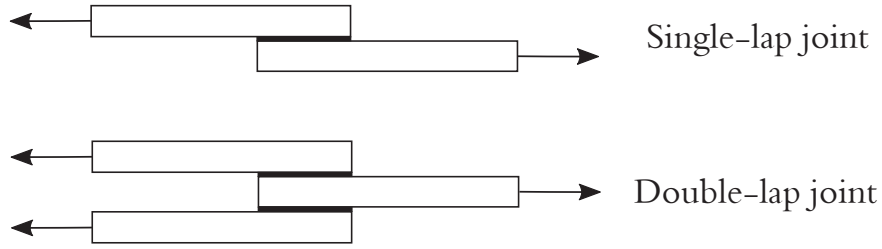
Géométrie : éprouvette single-lap et double-lap joint
